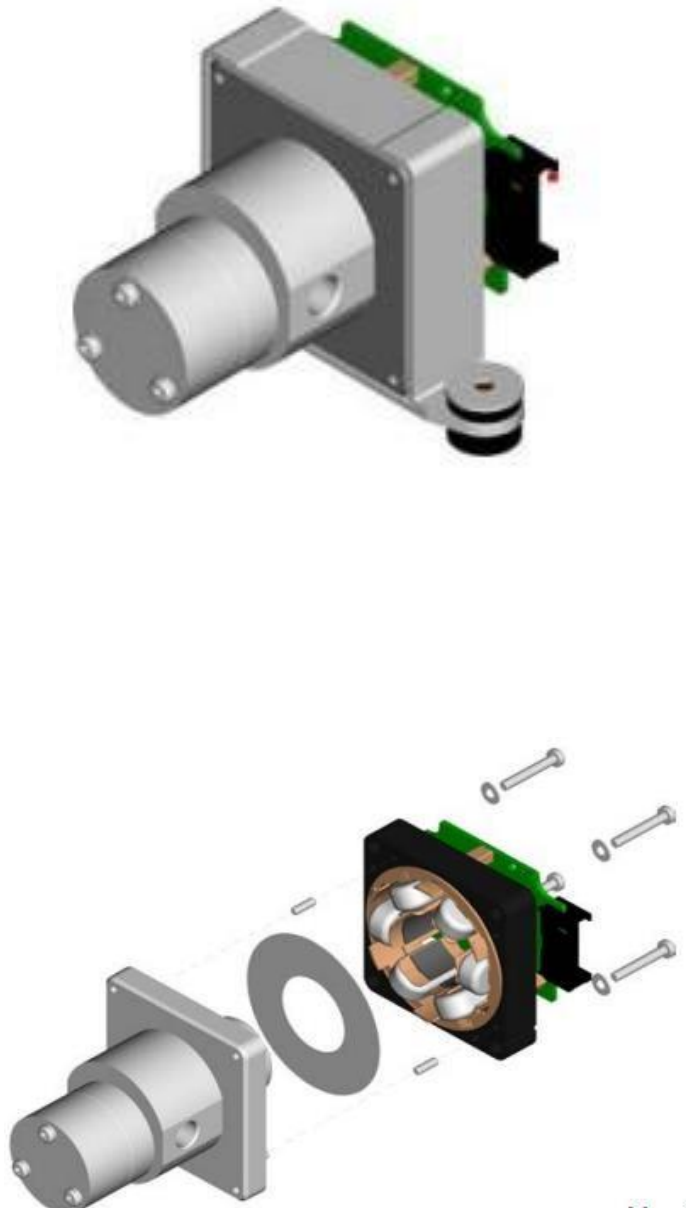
Ensamblaje de la bomba sin soporte electrónico.
